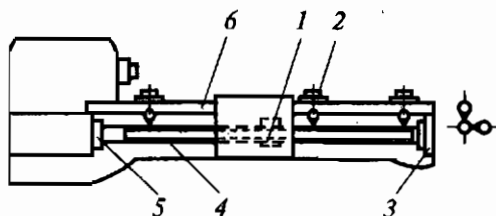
Схема проверки совмещения осей винта и разъемной гайки, а также параллельности винта направляющим станины: 1 — разъемная гайка; 2 — индикатор; 3 и 5 — подшипники; 4 — ходовой винт; 6 — направляющие станины
